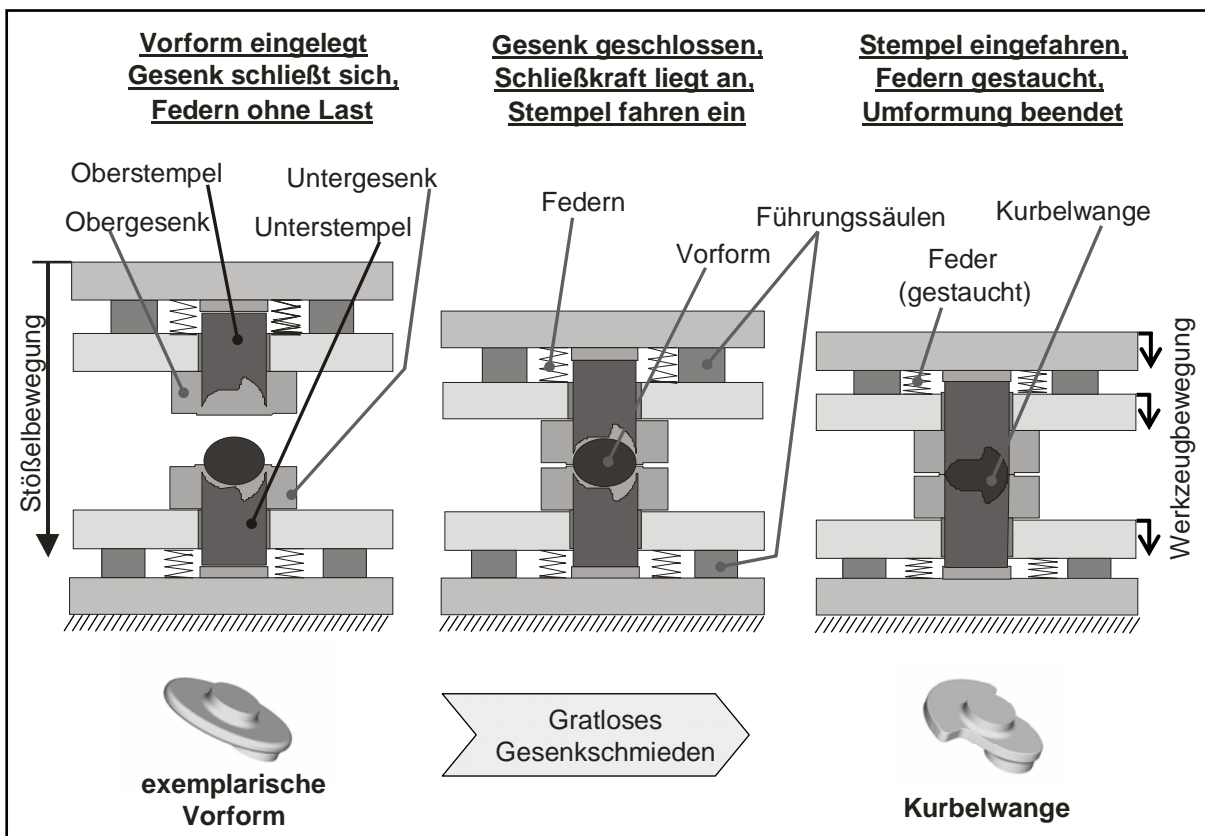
Werkzeugprinzip zum gratlosen Gesenkschmieden einer Einzylinderkurbelwelle
